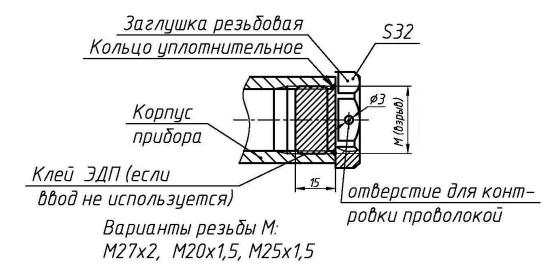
Элементы взрывозащиты при поставке оповещателя с резьбовыми заглушками
